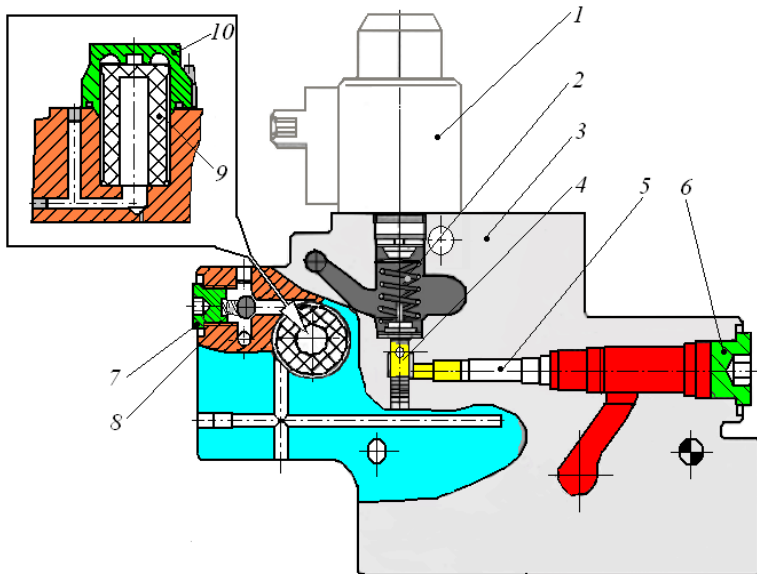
Концевая плита: 1 – включающий электромагнит редукционного клапана; 2 – пружина редукционного клапана; 3 – корпус; 4 – редукционный клапан; 5 – фильтр грубой очистки; 6 – заглушка фильтра грубой очистки; 7 – крышка перепускного клапана фильтра тонкой очистки; 8 – пружина перепускного клапана фильтра тонкой очистки; 9 – фильтр тонкой очистки; 10 – крышка фильтра тонкой очистки
